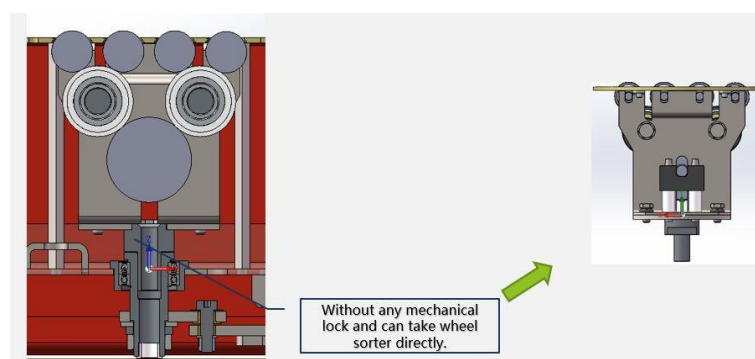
Конструкція механічного модуля колісного сортувальника
